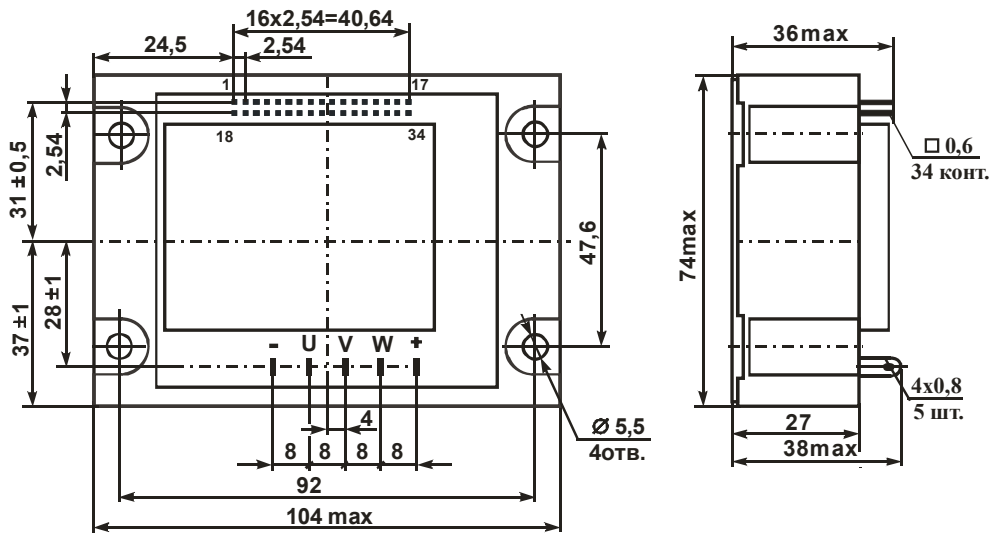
Габаритные размеры МУВДМ-5,10-1,2,6 тип силовой сборки «4»
